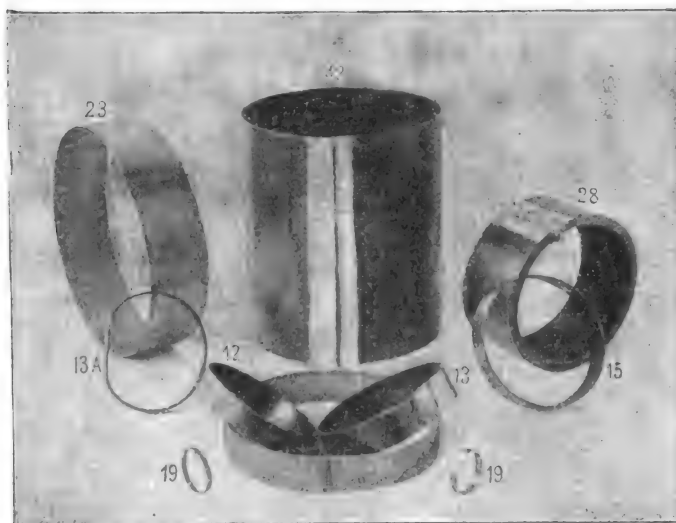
Soudure longitudinale de pièces d'acier.
